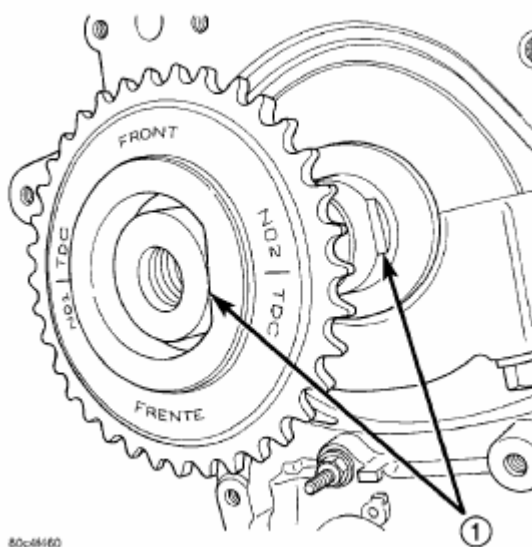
Центрирование звездочки привода балансировочного вала относительно коленчатого вала.
